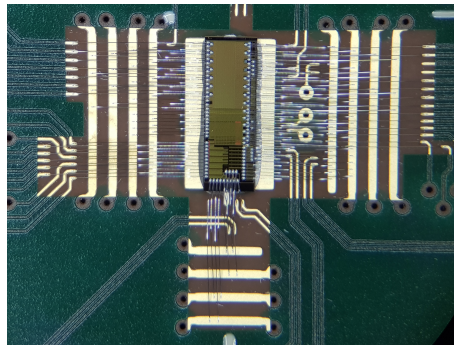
Detalle del chip Mini-MALTA soldado a la placa de pruebas
